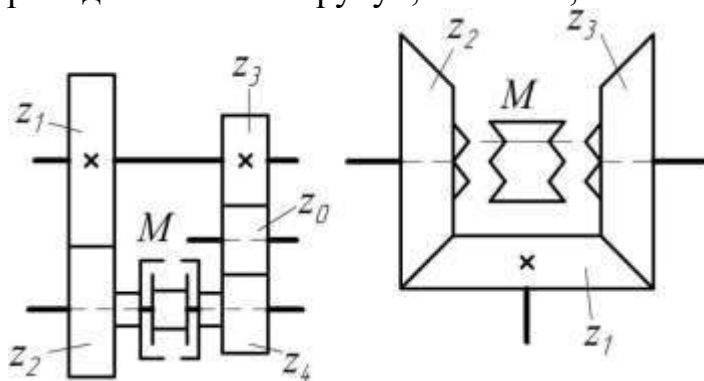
Реверсивні механізми металорізальних верстатів
